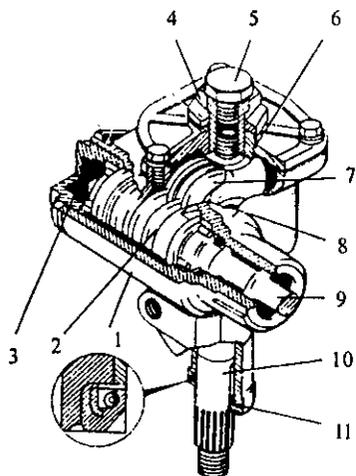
Редуктор рулевого механизма автомобиля Москвич-2141:
